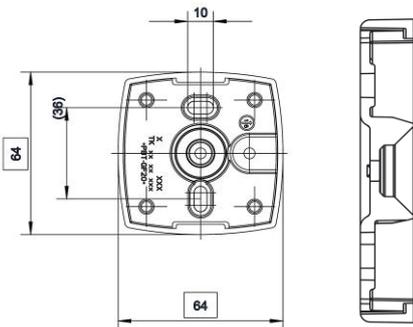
Draufsicht und Querschnitt der Adapterplatte
